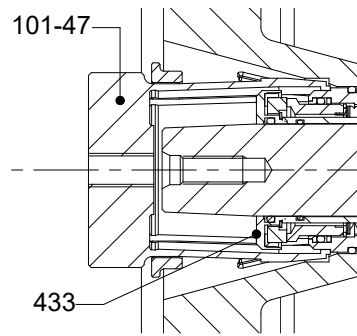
Montaje del cierre mecánico de cartucho doble C022/025M1-4STQ
